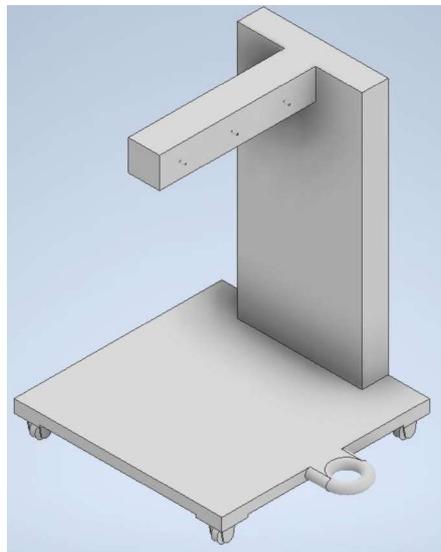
Carrito de soportes de cámara. Fuente: elaboración propia
